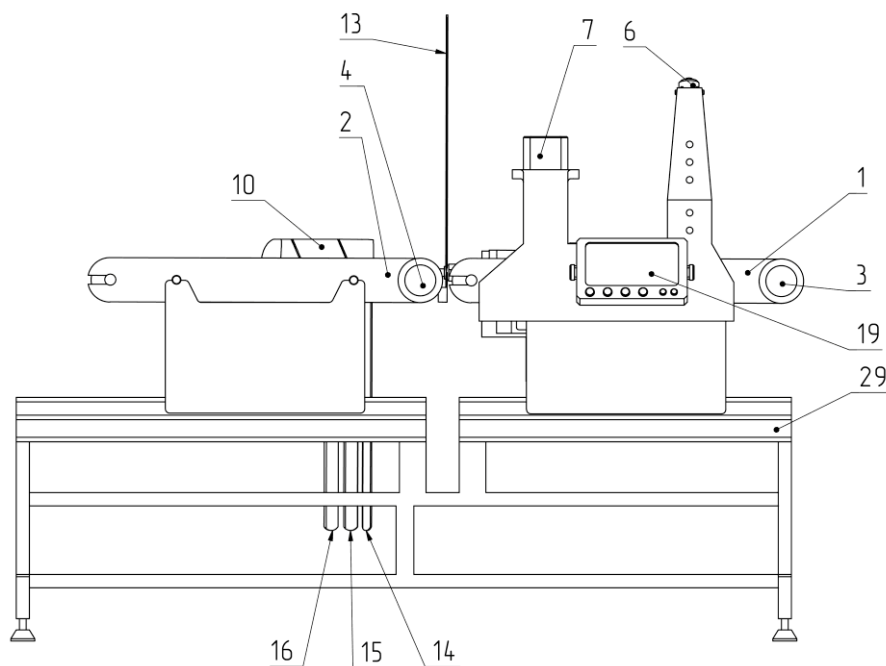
Устройство для резки рыбного филе (вид слева)
